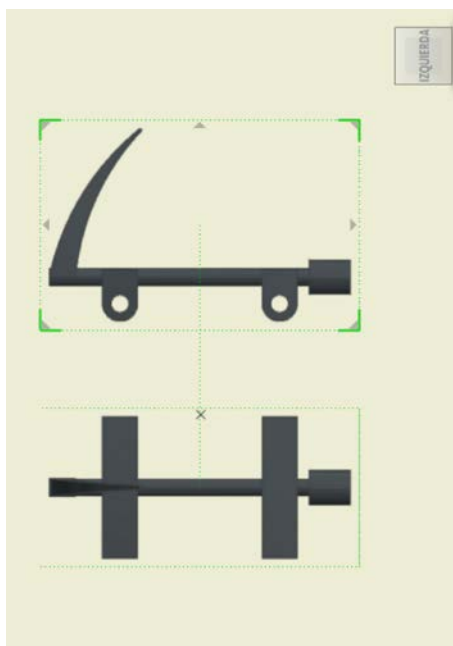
Vistas de alzado y planta superior de una pieza.
